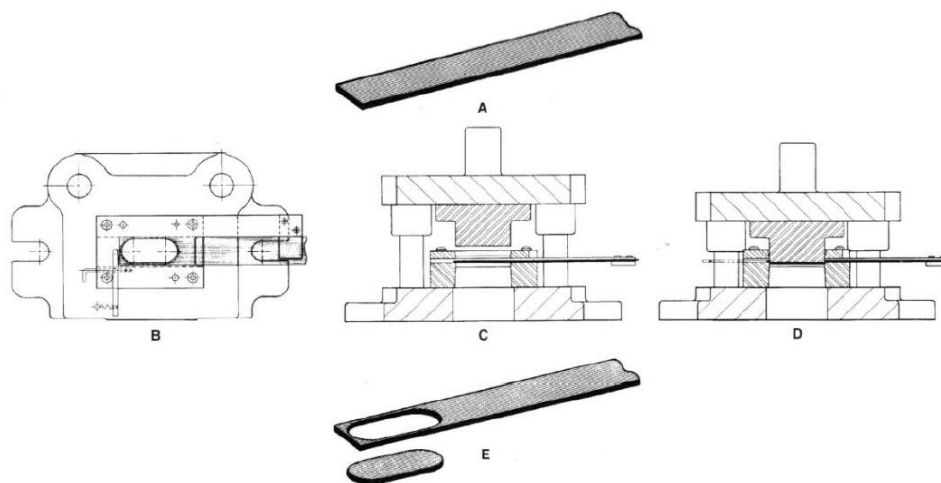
“Troquel de Corte: A. Tira de material. B. Vista superior del troquel. C. Troquel en posición abierta. D. Troquel en posición cerrada. E. Tira de material Troquelada. (Boljanaovic & Paquín, 2006)”
